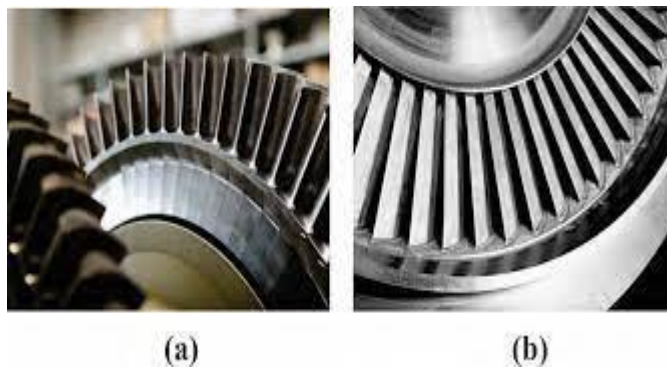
7 kontruktur rotor solid dan built -up rotor
